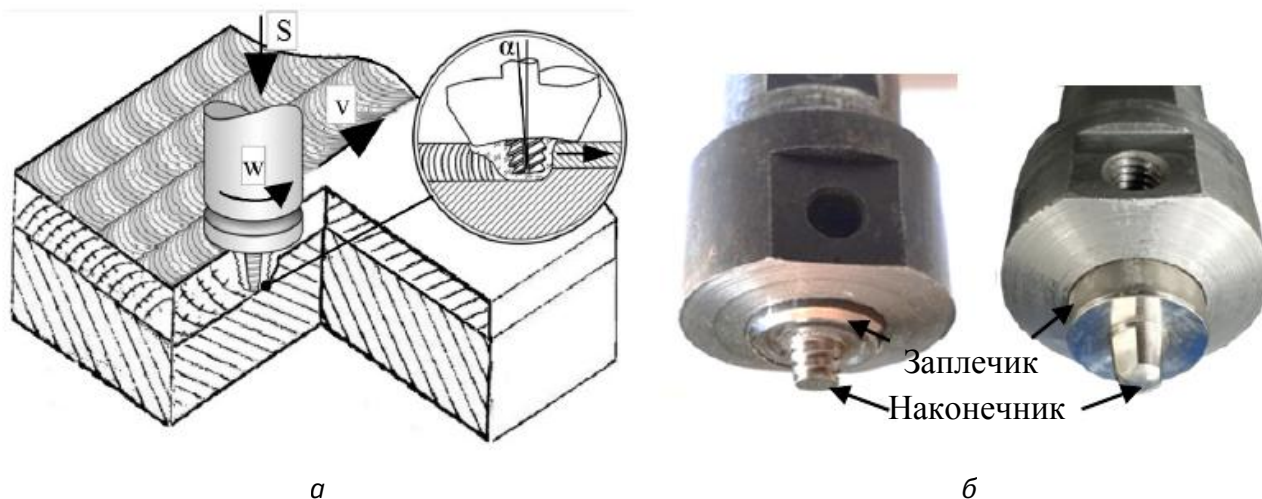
Схема процесса сварки трением с перемешиванием (а) и сварочный инструмент (б):
